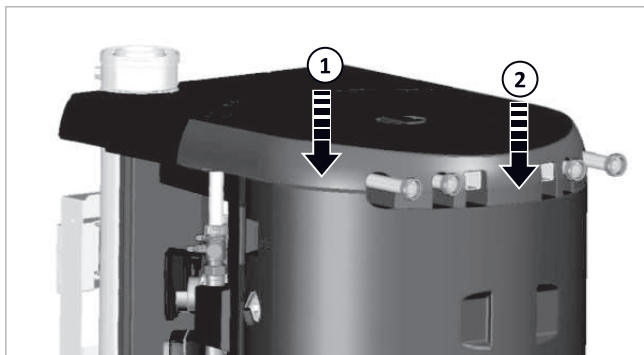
Bovenste isolatiedelen met de aansluitingen van bovenaf
